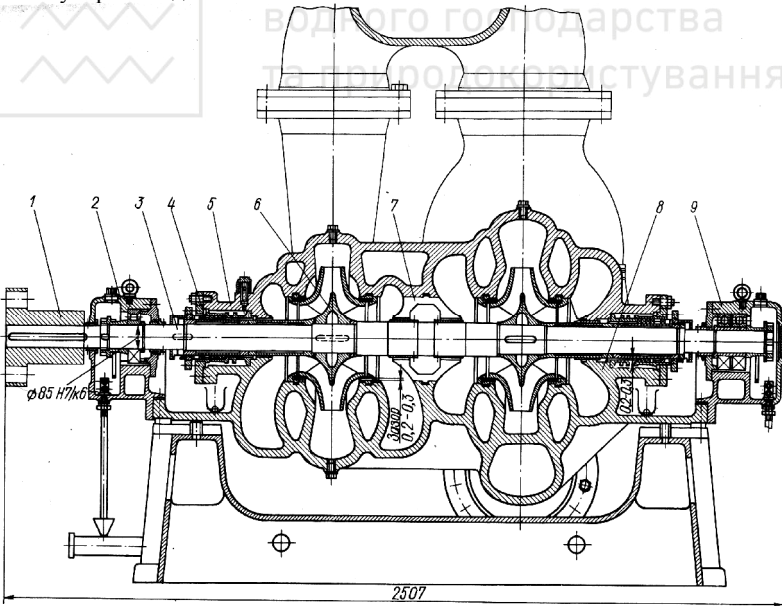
Насос мережний СЭ 1250-140: 1- муфта; 2- роликовий підшипник; 3- ротор; 4- кінцеве ущільнення; 5- кришка корпуса; 6- колесо; 7- діафрагма; 8- нижня частина корпуса; 9- радіально-упорний підшипник.
